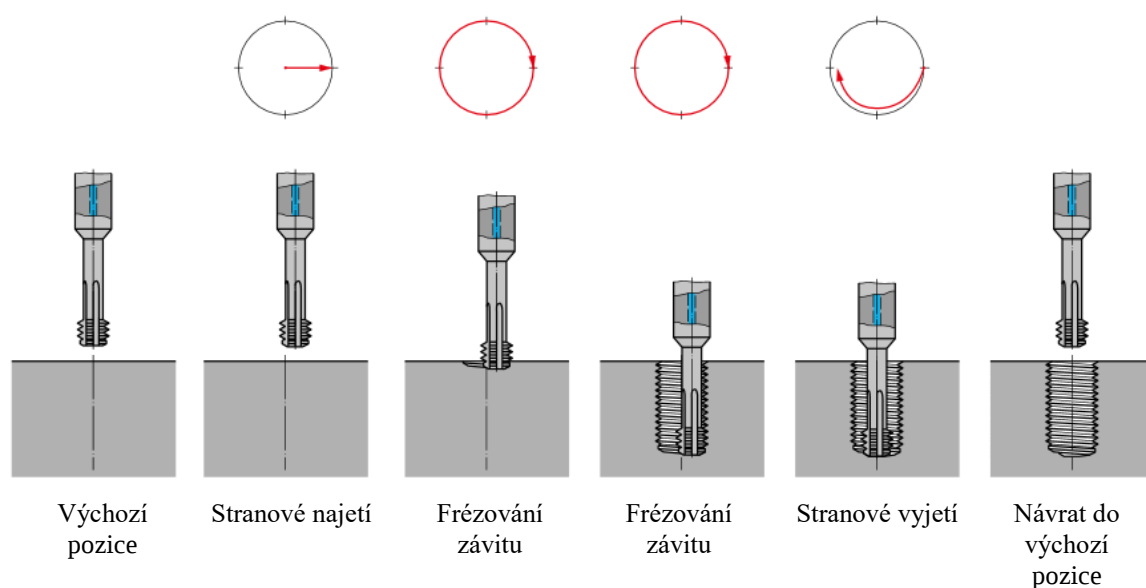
Princip frézování závitu pomocí stopkové frézy [12].
